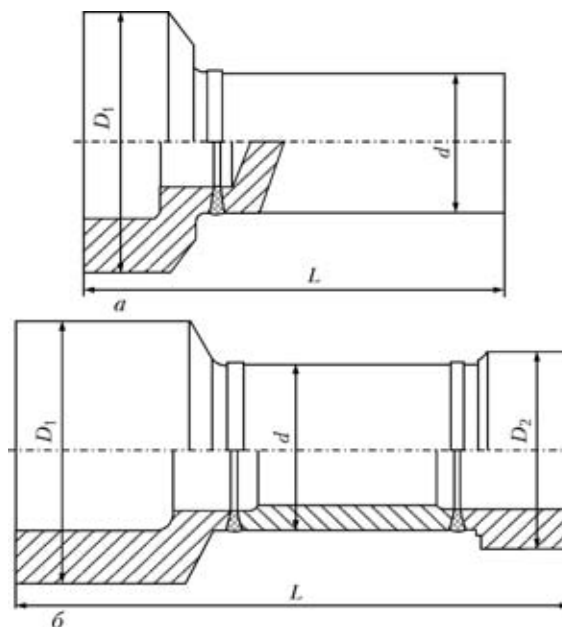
Схемы сварных заготовок шлицевого (а) и шарнирного (б) валов
